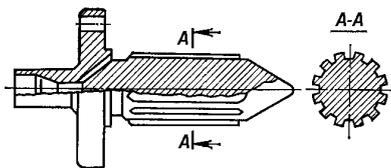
Торпеда нагревательного цилиндра плунжерных пластикаторов
